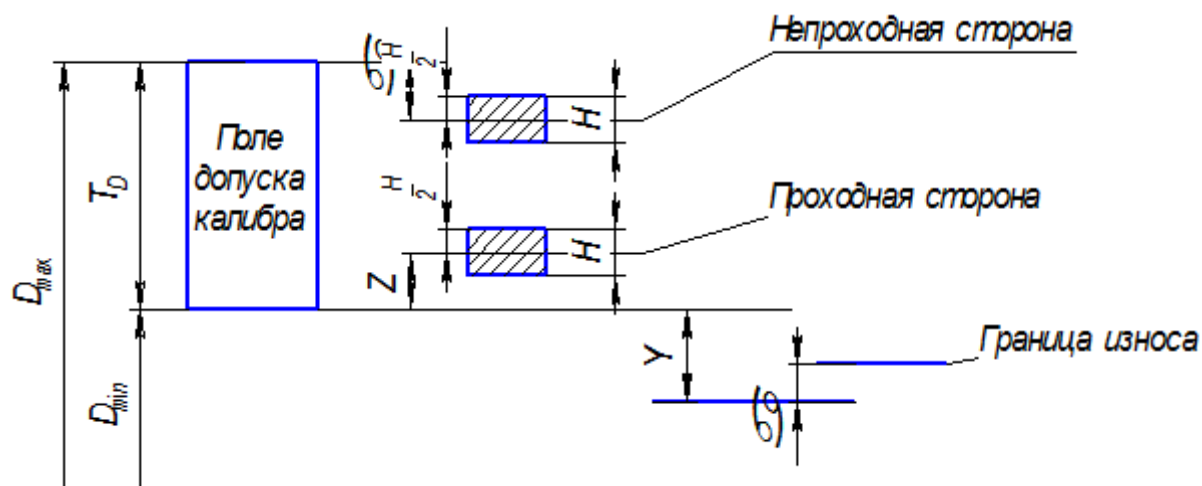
Схема расположения полей допусков калибров для контроля отверстий
